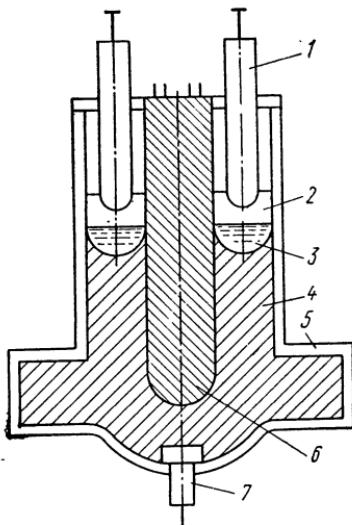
Схема электрошлакового получения отливки «Корпус запорной арматуры высокого давления»:
